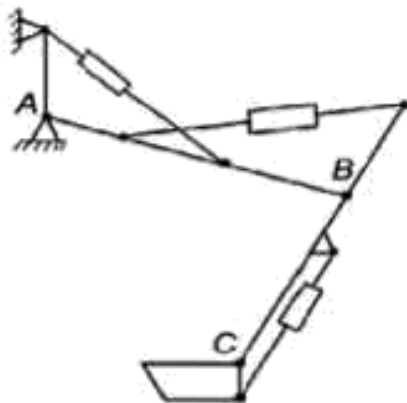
Схема рабочего оборудования одноковшового экскаватора
